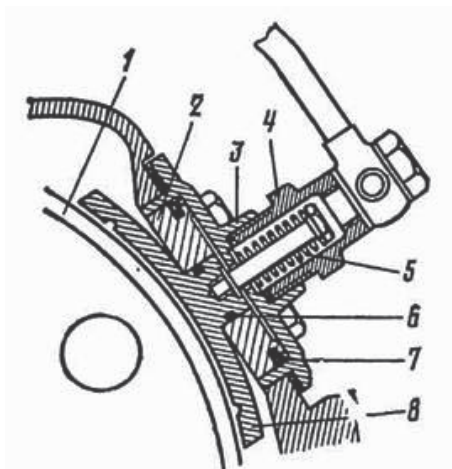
Тормоз-синхронизатор (Примечание: ведомый барабан фрикциона (1); поршень (2); корпус (3); штуцер (4); пружина (5); резиновое уплотнительное кольцо (6); резиновая манжета (7); тормозная колодка (8)).
